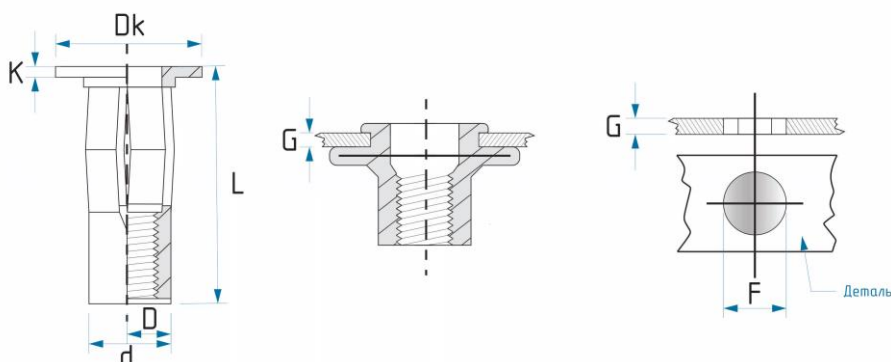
Заклёпка резьбовая щелевая, стандартный борт
